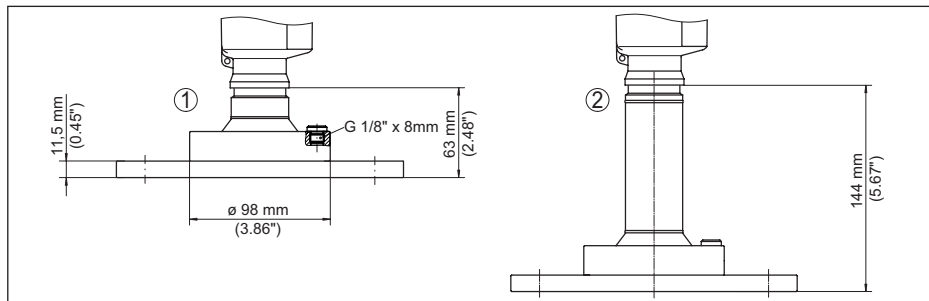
VEGAPULS 6X, flangia con antenna a lente (spessore della flangia v. disegno, dimensioni della flangia conformemente a DIN, ASME, JIS)
